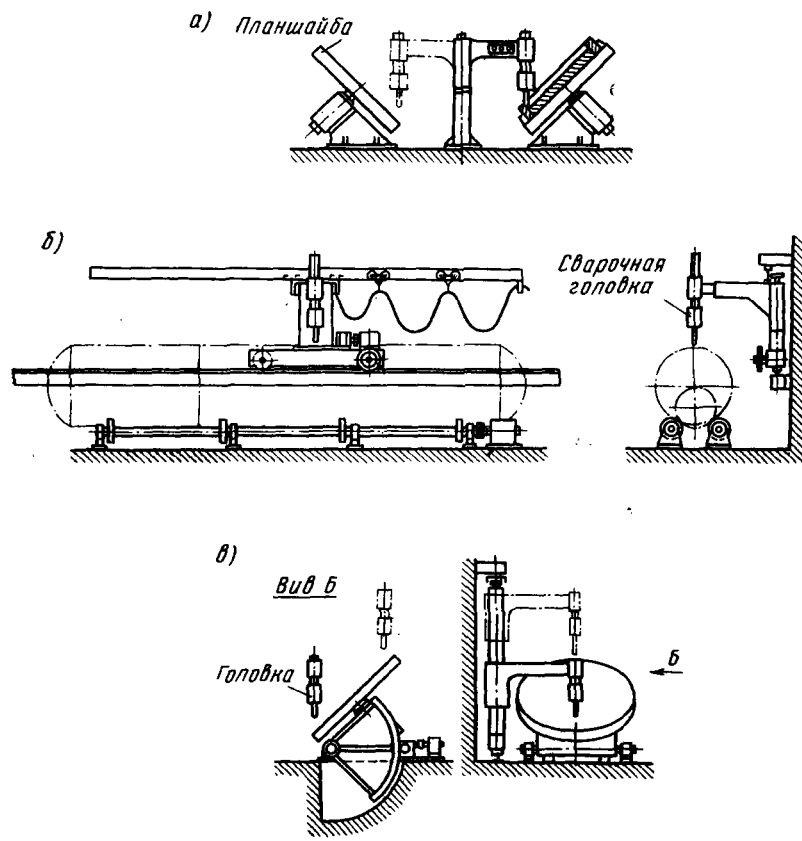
Основные типы сварочных приспособлений:
